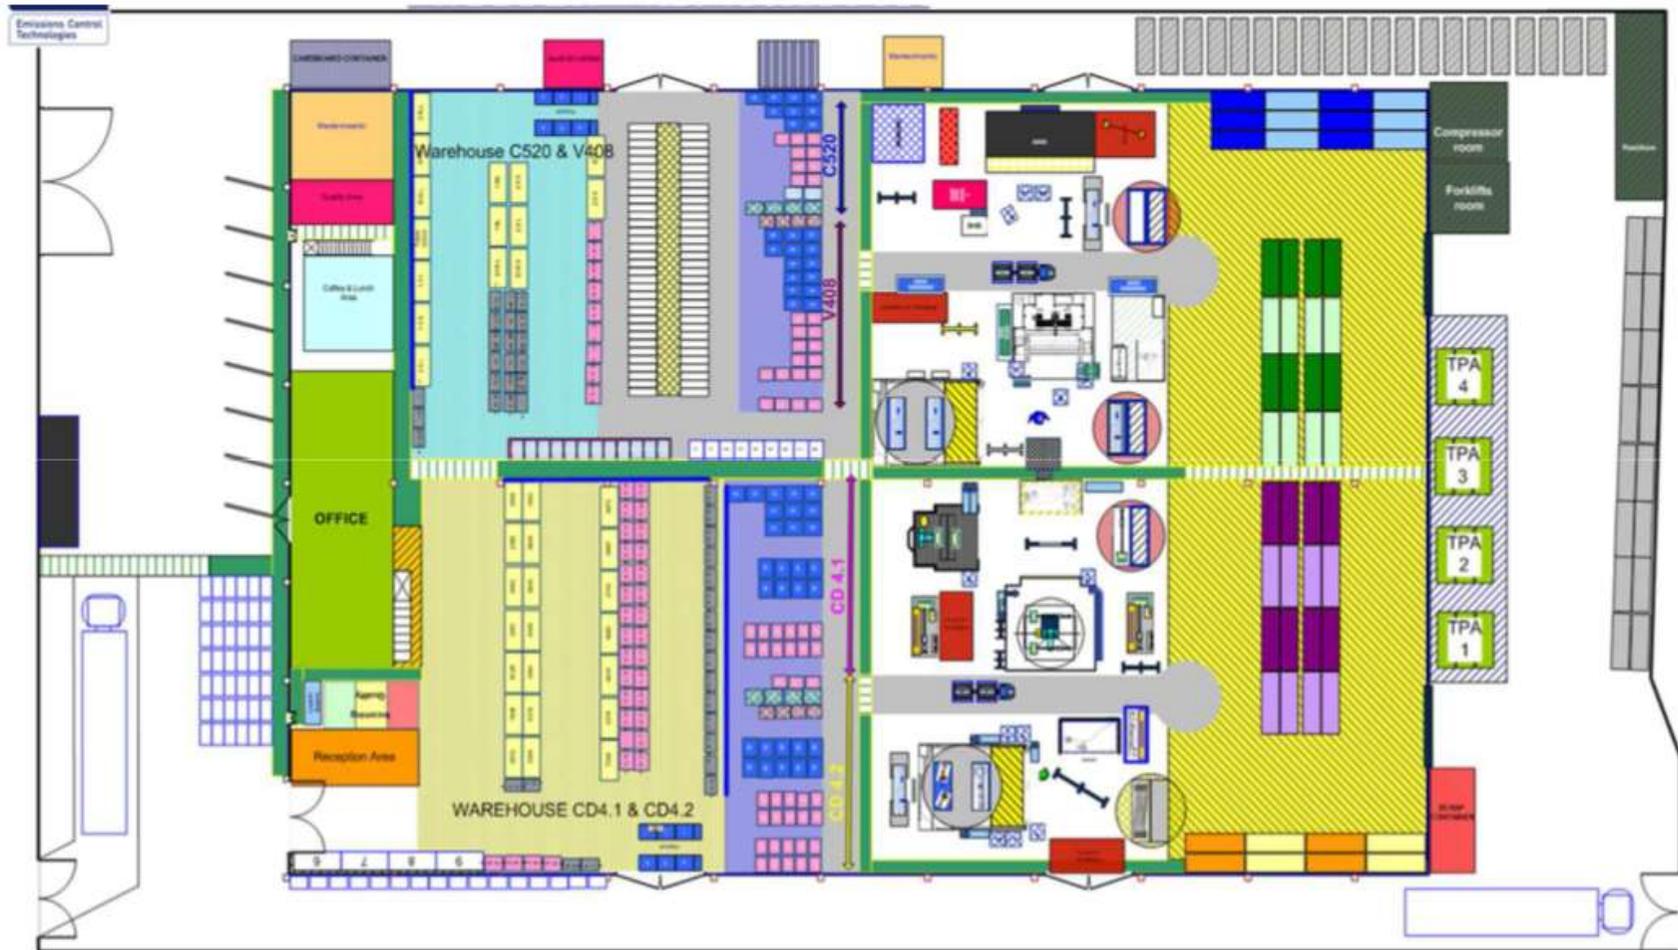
Layout de la planta. Recuperado de: 'Manual de acogida planta Almussafes Faurecia Escapes' (2017)
